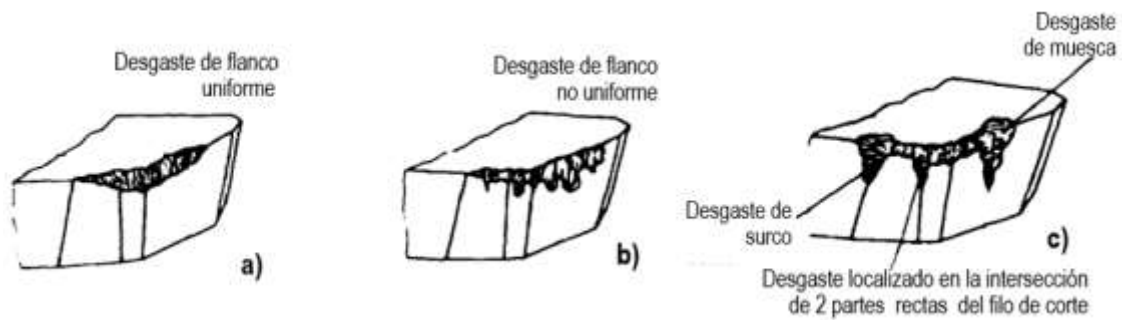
Desgaste del flanco de un inserto de carburo en operación de fresado: a) VB1; b) VB2 y c) desgastes localizados VB3. [92]
